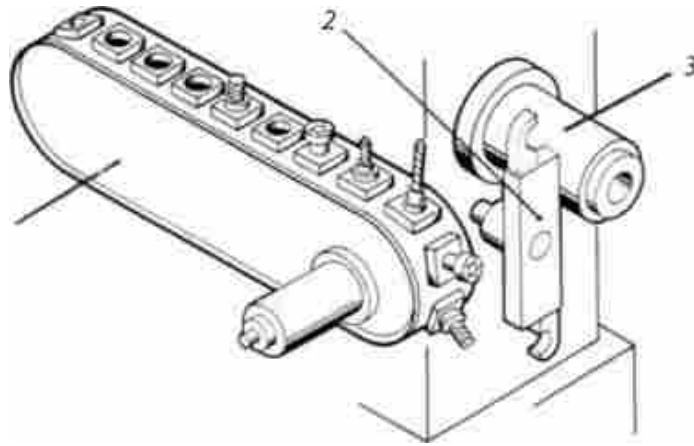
Схема зміни інструменту з магазину автооператором:
